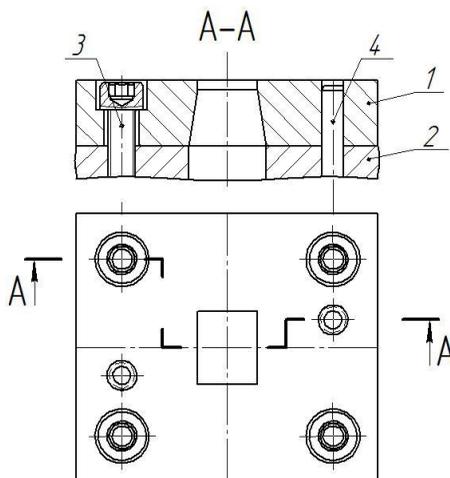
Крепление плитовой матрицы: 1 – матрица; 2 – плита; 3 – винт; 4 – штифт
